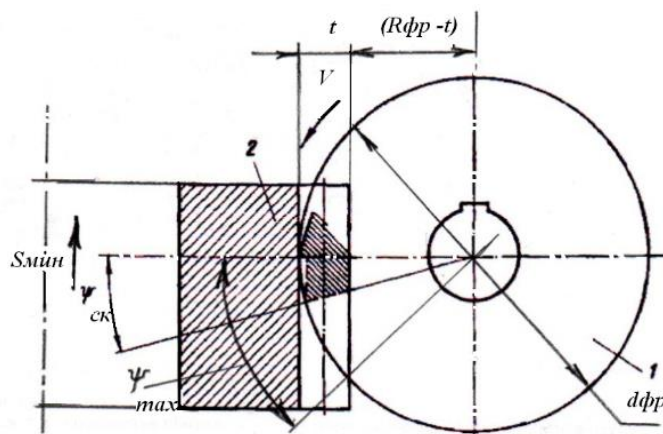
Схема розрахунку параметрів обробки при зубофрезеруванні зубчастих коліс
